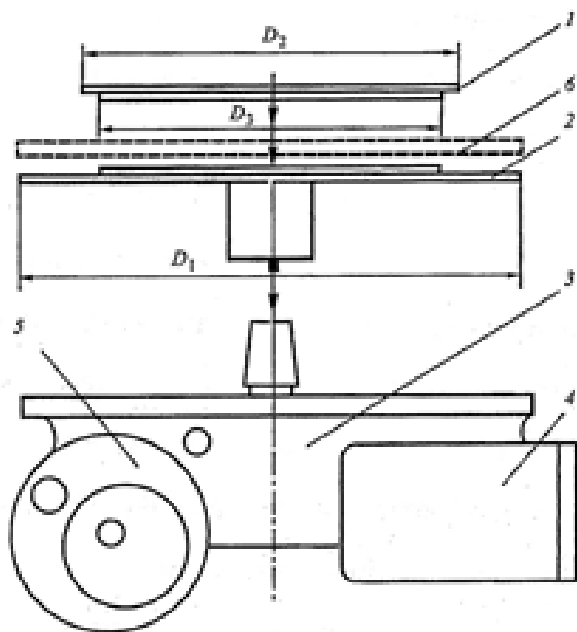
Устройство для напыления дисков: 1 – крышка, 2 – основание, 3 – редуктор, 4 – электродвигатель для обеспечения поворота диска при напылении фрикционного материала, 5 – ручной привод, 6 – фрикционный диск, D_1 , D_2 , D_3 – размеры устройства для напыления. Стрелками показаны связи узлов и деталей.
